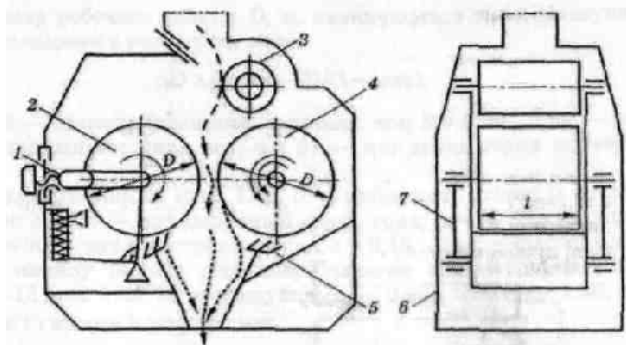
Функціональна схема вальцювого верстата млина: 1 – механізм регулювання зазору; 2 – тихохідний валець; 3 – живильний валець; 4 – швидкохідний валець; 5 – щітка; 6 – корпус; 7 – балансир.
